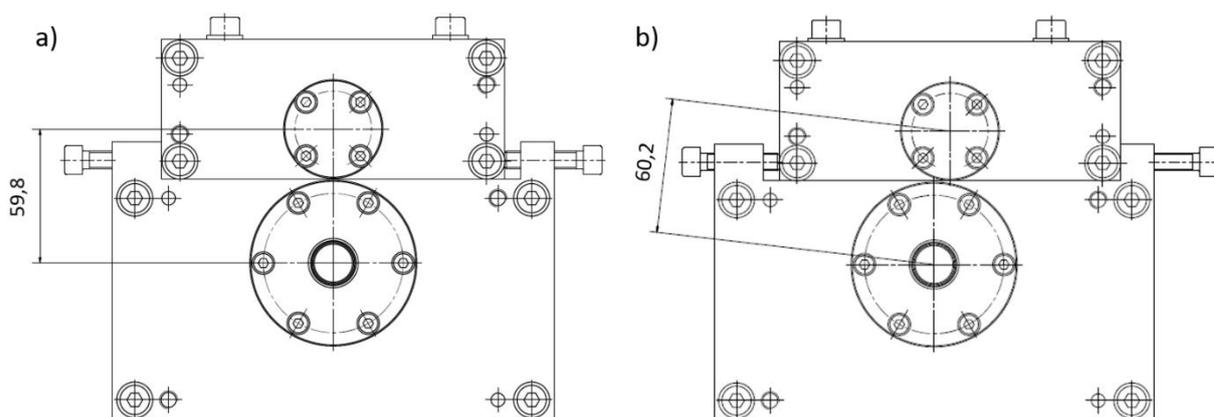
Konstrukcja pierwszego prototypu toczonej przekładni mimośrodowej
